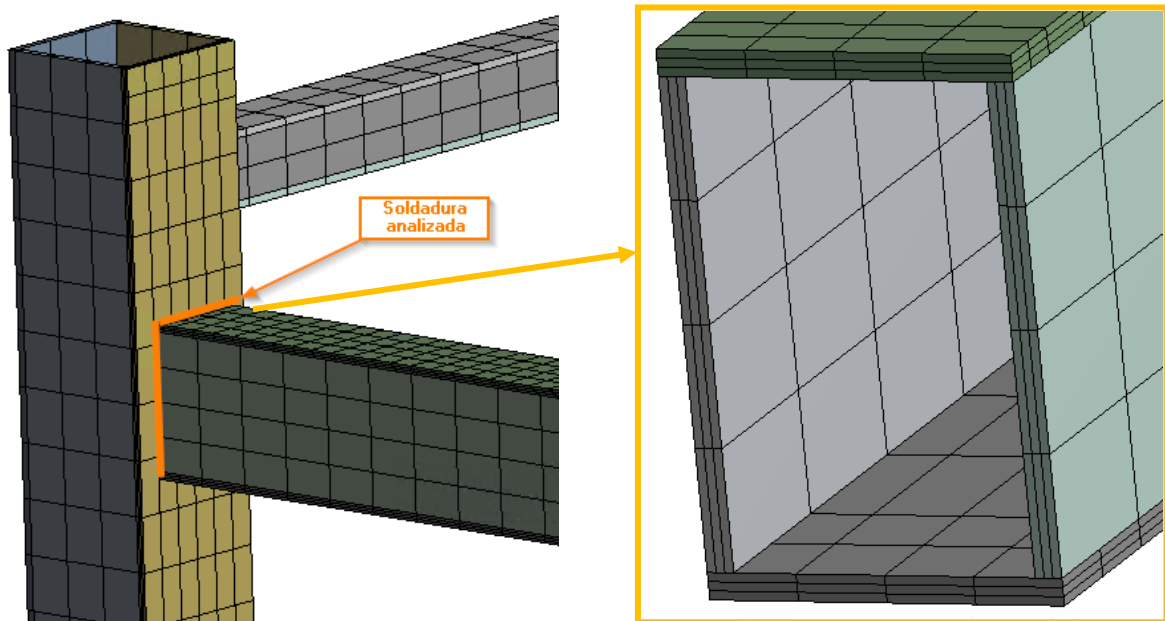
Soldadura analizada a fatiga y detalle de la malla en ANSYS.
